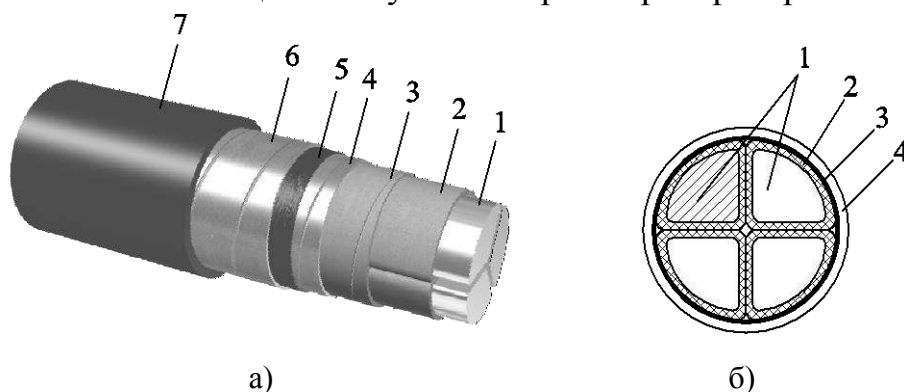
Конструкции силовых кабелей напряжением до 10 кВ: а – трехжильный кабель напряжением 10 кВ. 1 – жила; 2 – фазная изоляция; 3 – поясная изоляция; 4 – металлическая оболочка; 5 – защитные и упрочняющие покрытия; 6 – броня из двух стальных лент; 7 – наружный защитный покров; б – четырехжильный кабель с пластмассовой изоляцией на напряжение 1 кВ. 1 – жила; 2 – фазная изоляция; 3 – поясная изоляция; 4 – защитная оболочка
